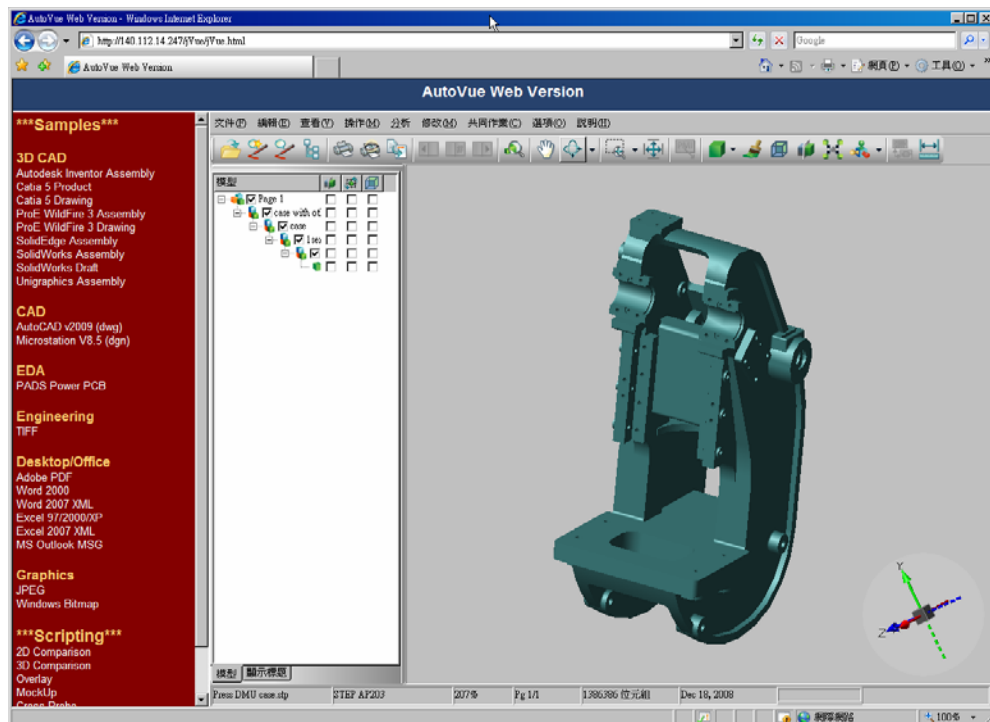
直接在使用者端開啟網頁讀取 CAD 模型
